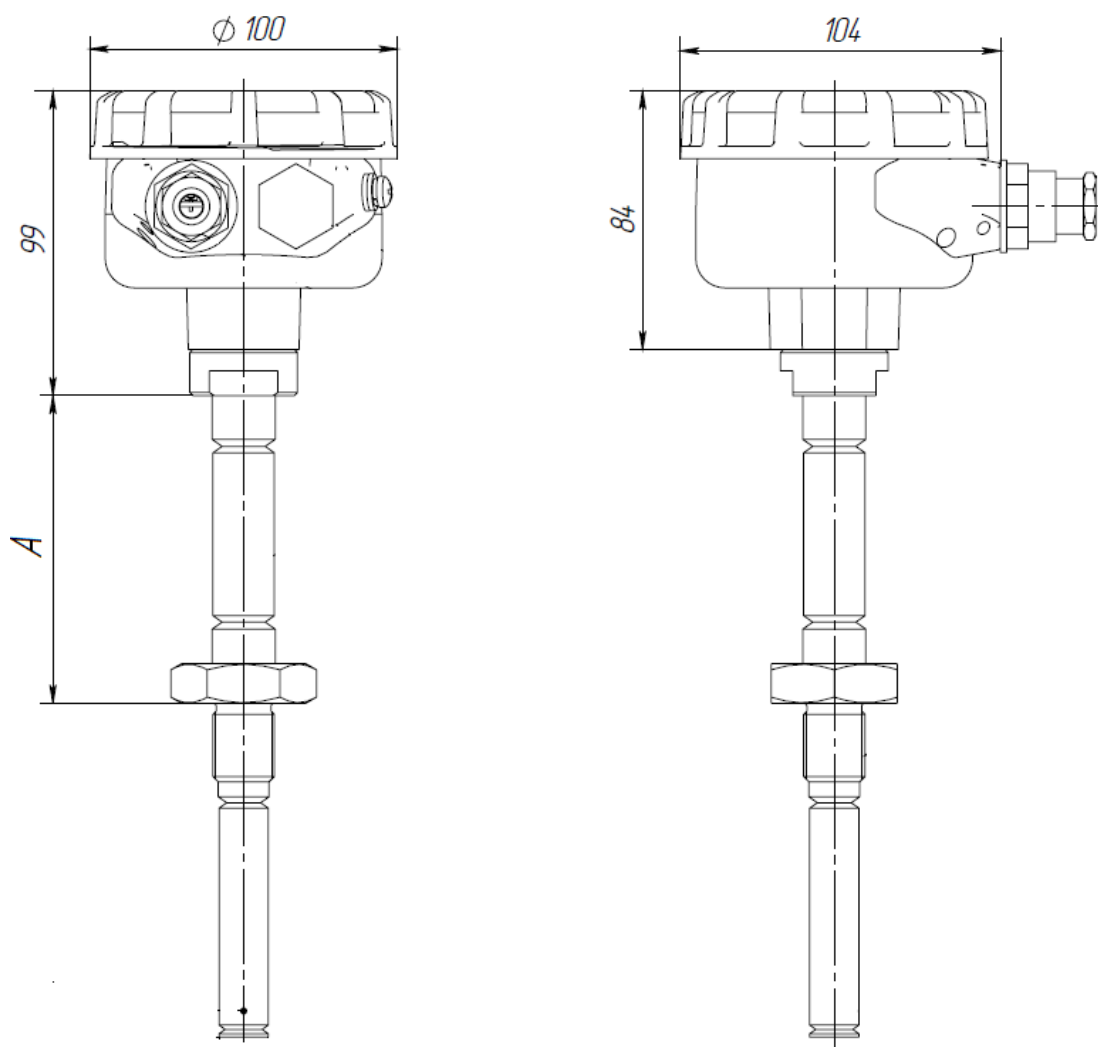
Габаритные размеры корпуса сигнализатора
